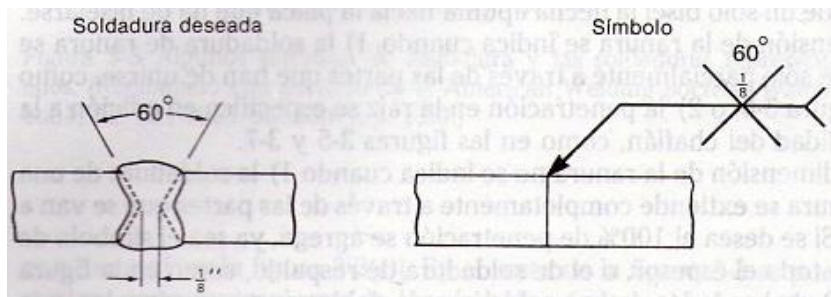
Símbolo de la soldadura en el que se especifica una soldadura de doble ranura con ambas ranuras de las mismas dimensiones.
